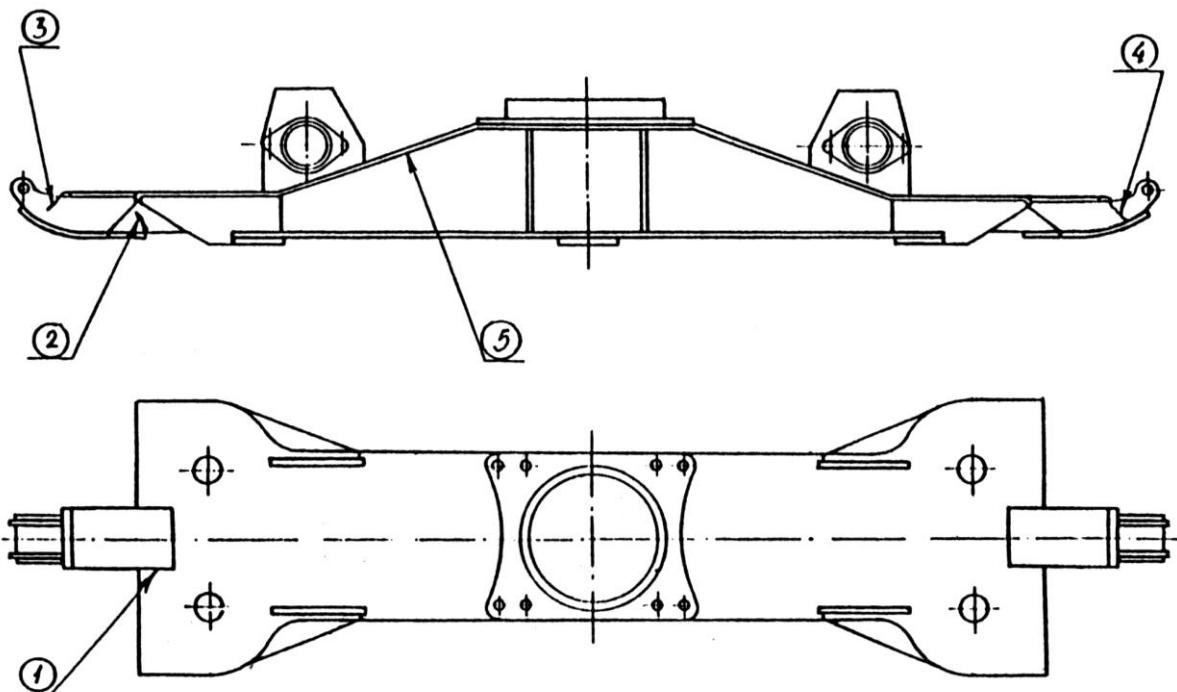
Основные дефекты балки надрессорной тележки КВЗ-5, ремонтируемые сваркой или наплавкой
